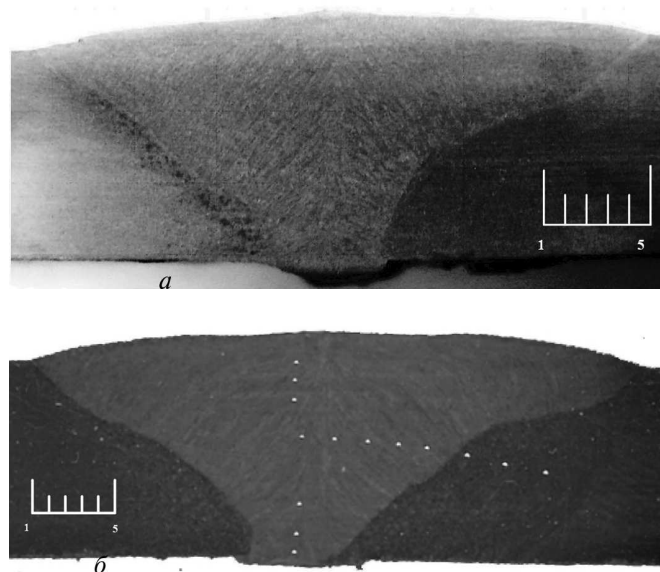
Макроструктура шва, выполненного двухдуговой сваркой под флюсом, без предварительной засыпки порошков (а) и с предварительной засыпкой порошков (б)
